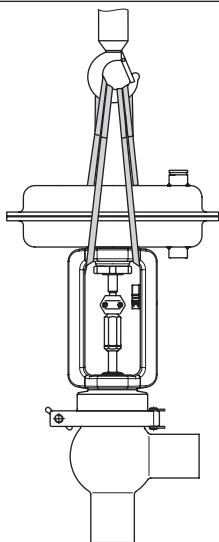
Type 3347 avec type 3271 sans anneau de levage
